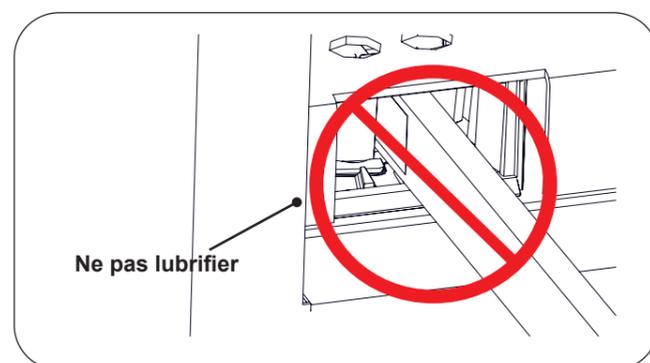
Ne pas lubrifier la poutre ou le mécanisme de verrouillage
